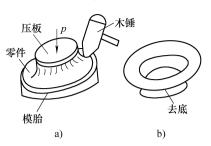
收边成形内弯边 a) 在模具上收边 b) 零件
